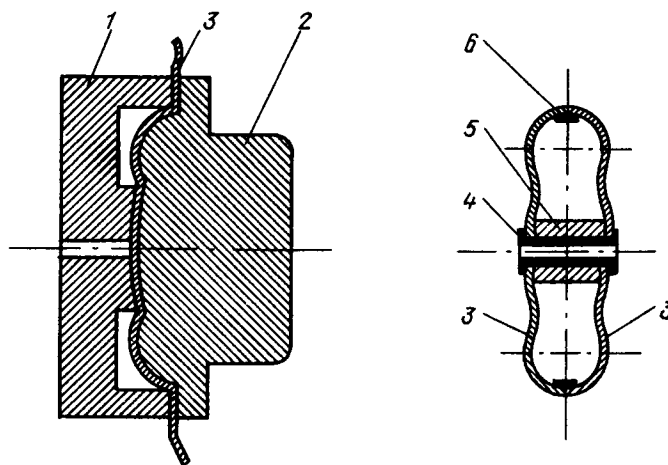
Пресс-форма для изготовления колеса из пластмассы и разрез готового колеса:
